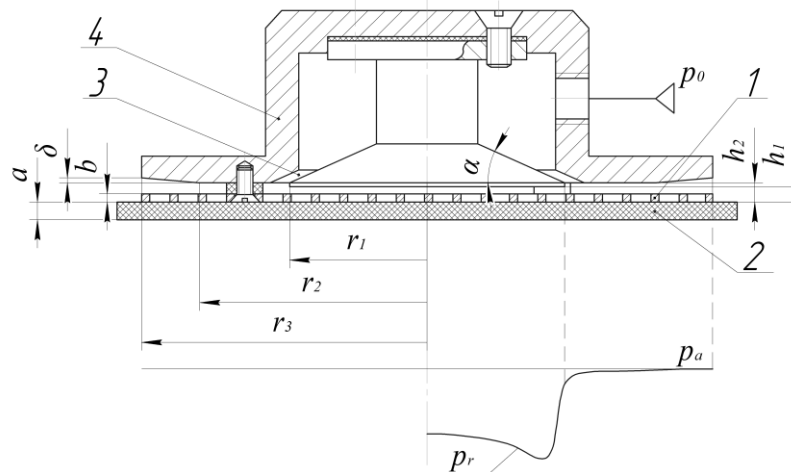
Конструктивна схема струминного захоплювача для деталей з текстилю
